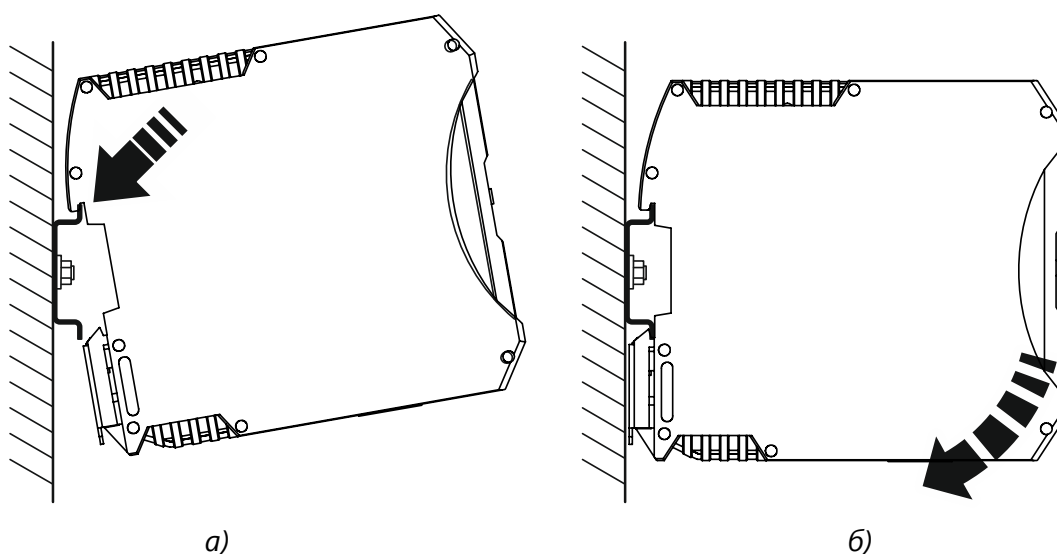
Установка IPN-1LE на DIN-рейку
